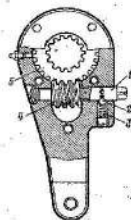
Рычаг тормоза: 1 — ось червяка; 2 — шарик иксатора; 3 — грузина; 4 — червяк; 5 — червячная шестерня.
